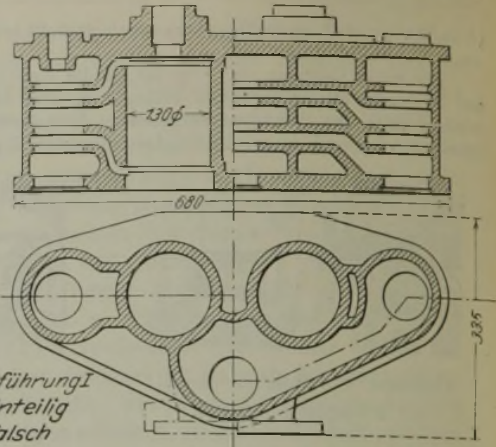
Umsteuerzylinder einer Schiffsmaschine.
